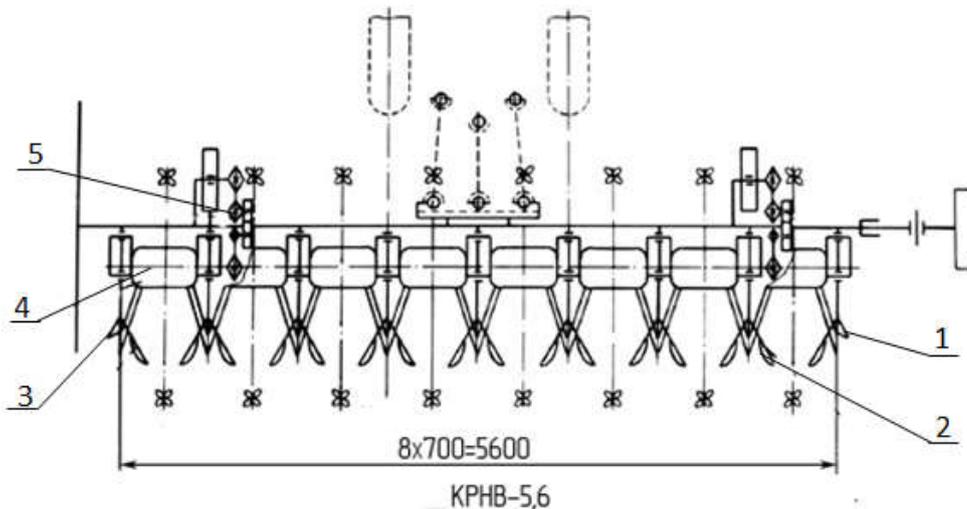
Схема розташування корпусів борозноарізувальних під час роботи з пристроєм для внесення твердих мінеральних добрив для міжрядь 70 см:
